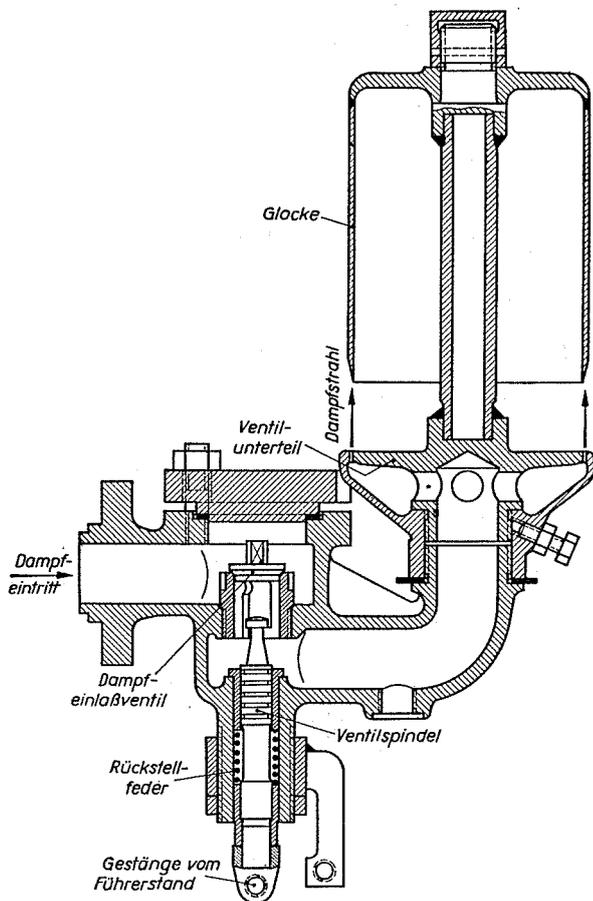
Dampfpfeife mit fest geführtem Kegelventil
